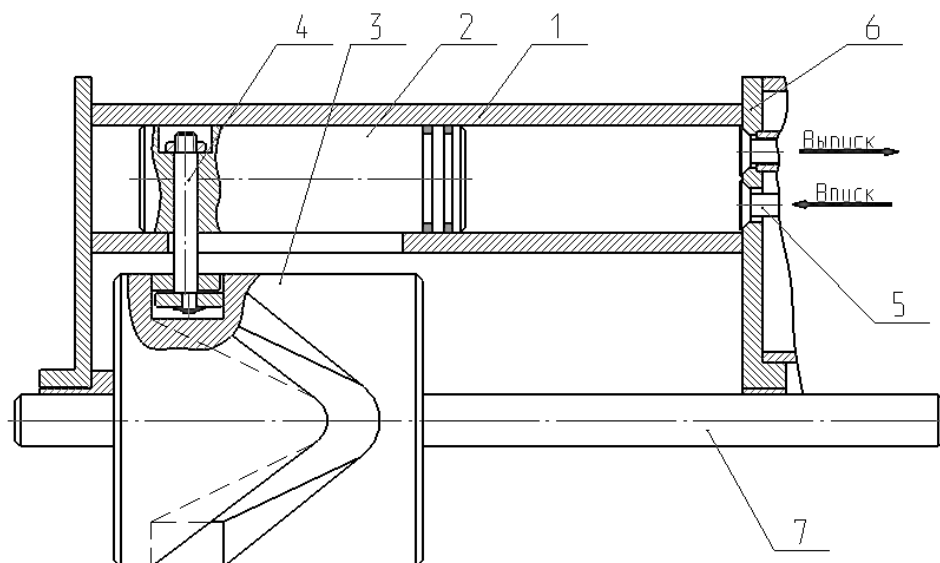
Схема работы одного из цилиндров пневмопривода: 1 – рабочий цилиндр, 2 – поршень с уплотнительными кольцами, 3 – приводная втулка, 4 – ось с роликами, 5 – клапаны, 6 – корпус, 7 – приводной вал
